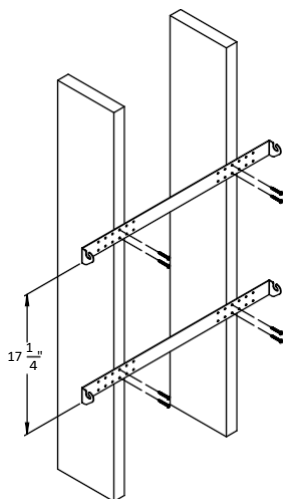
INSTALLATION VERTICALE SUR UN MUR OU UN PANNEAU
